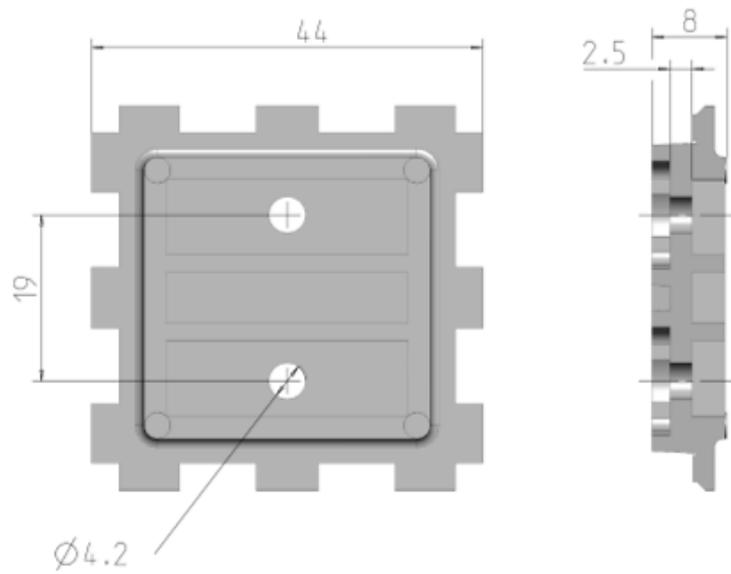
Draufsicht und Querschnitt von der Adapterplatte
